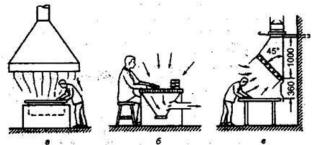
Вытяжная вентиляция на сварочном посту
